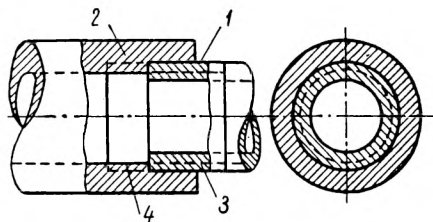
Резьбовое соединение двух деталей (болта с гайкой).
